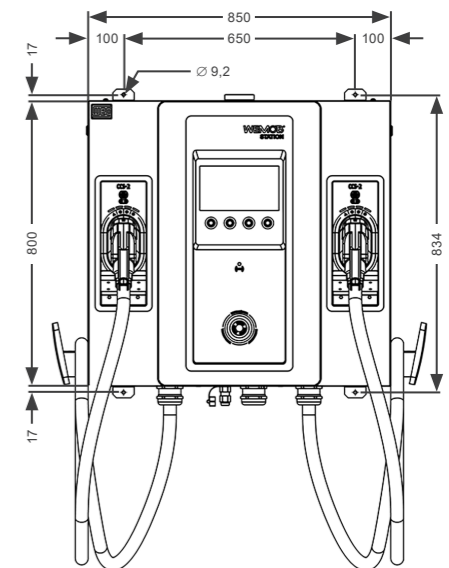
Dimensões da WEMOB-STATION (60/80 kW) para a fixação à estrutura de concreto - mm
